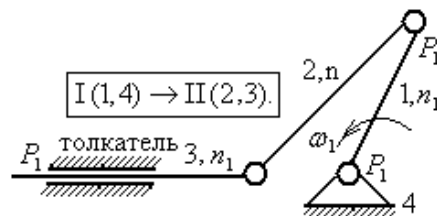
Схема механизма, заменяющего самоустанавливающийся трехзвенный кулачковый механизм с поступательно движущимся толкателем
